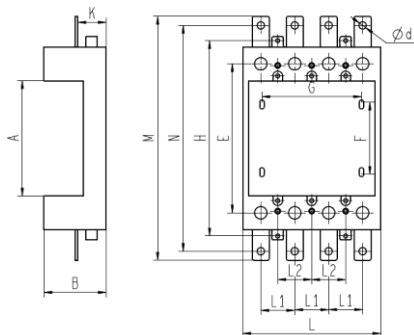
Габаритные размеры корзины втычного фронтального подключения КА-300
